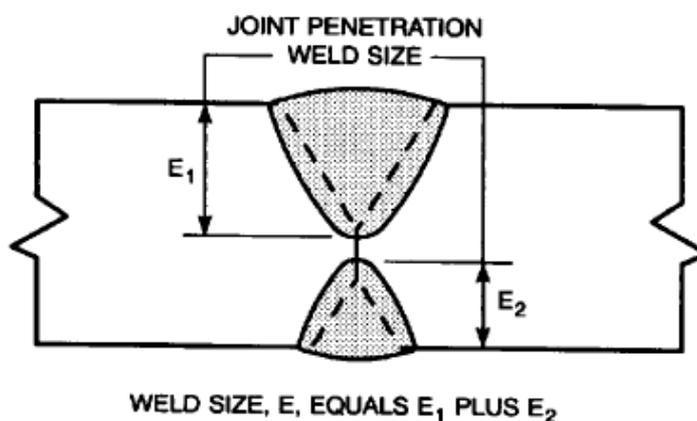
Soldadura de ranura con junta de penetración parcial.
